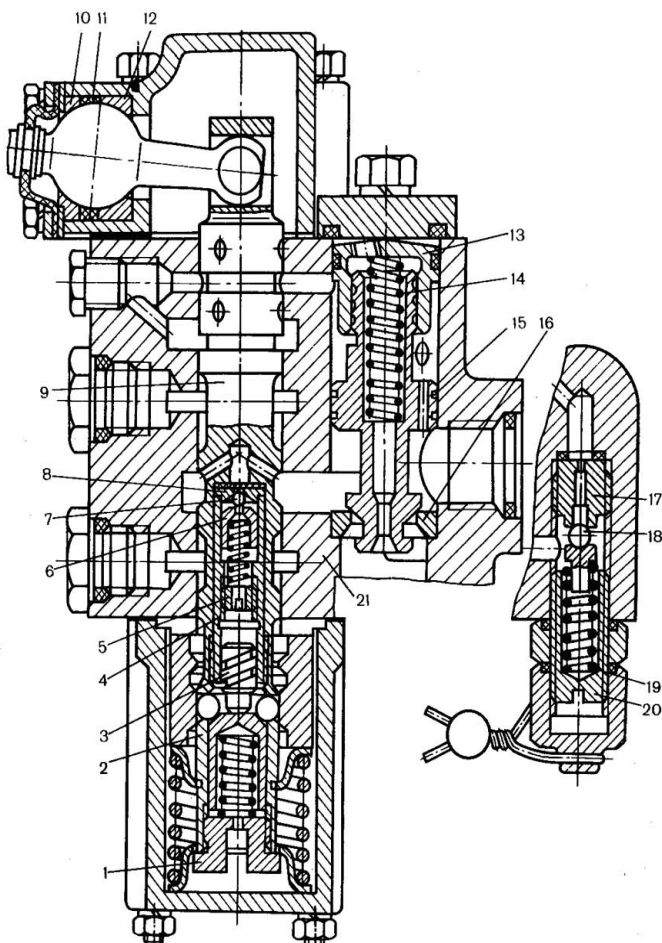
Золотниково-клапанный распределитель: 1 — пробка; 2 — обойма фиксаторов; 3 — плунжер; 4 — гильза; 5 — регулировочная пробка; 6 — упор; 7 — запорный клапан; 8, 16 — седло; 9 — золотник; 10, 12 — гнезда рычага; 11 — уплотнение; 13 — направляющая; 14, 19 — пружина; 15 — перепускной клапан; 17 — гнездо предохранительного клапана; 18 — шарик; 20 — регулировочный винт; 21 — корпус
